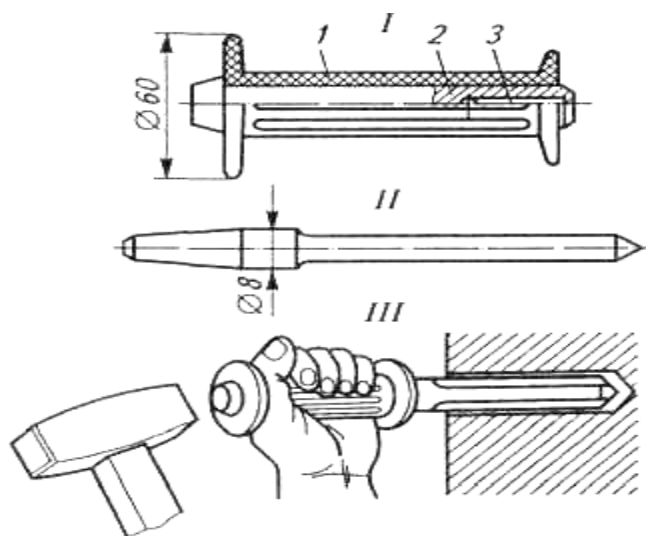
Пробивка гнезд ручным пробойником и оправкой:
